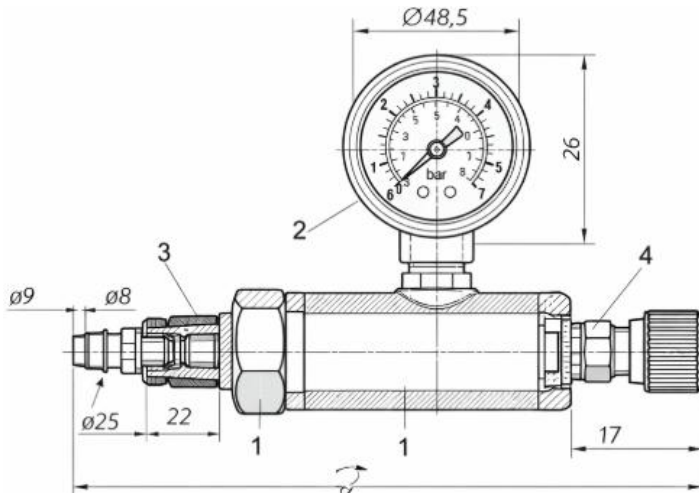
1 Пристрій для вимірювання тиску палива: 1 – корпус; 2 – манометр; 3 – адаптер; 4 – запірний клапан
